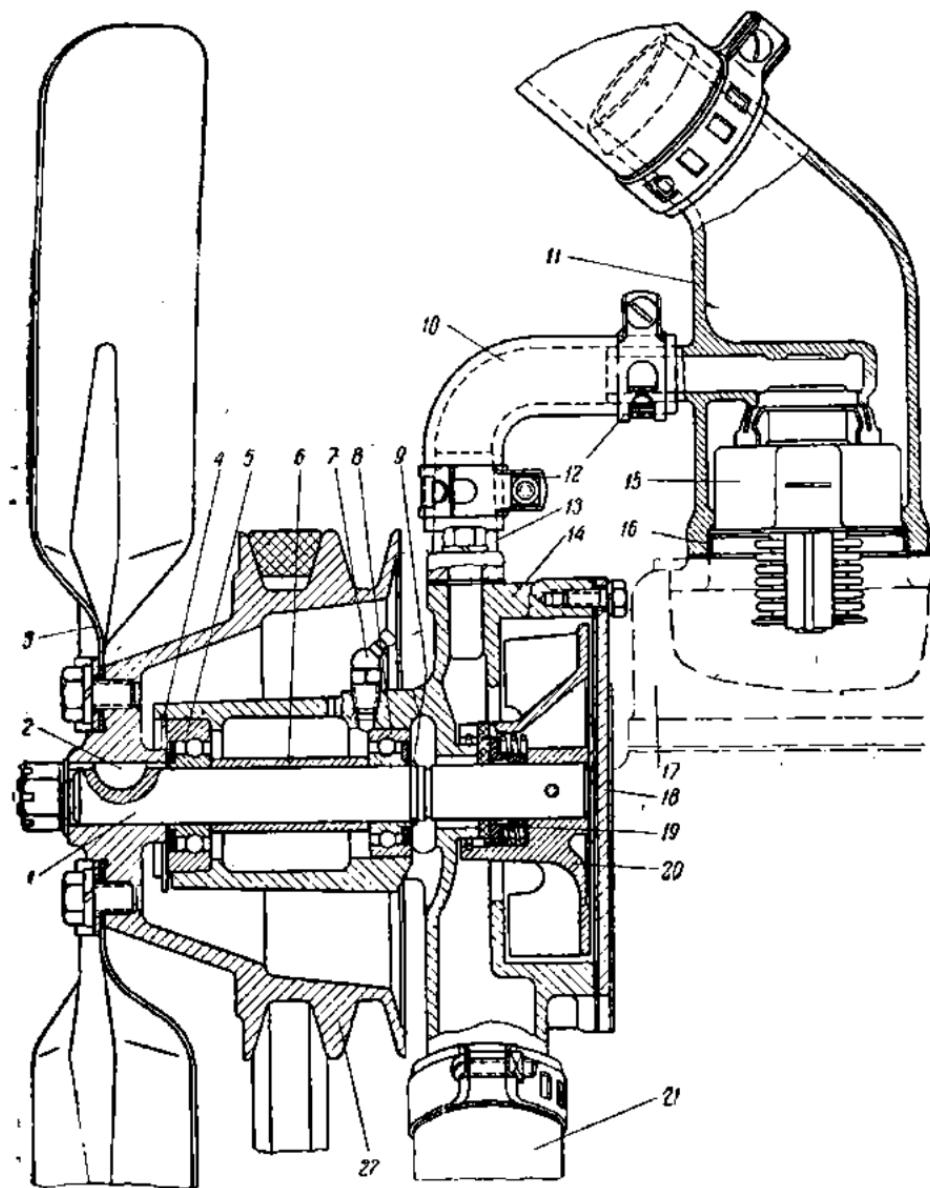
Элементы системы охлаждения (1 — вал насоса и вентилятора; 3 — вентилятор; 5 и 8 — подшипники вала; 7 — масленка; 10 — обходная трубка (шланг); 11 — выходной патрубок; 14 — корпус насоса; 15 — термостат; 17 — головка блока; 18 — крышка корпуса насоса; 19 — уплотняющая резиновая втулка; 20 — крыльчатка насоса; 21 — шланг, подающий воду; 22 — шкив).
